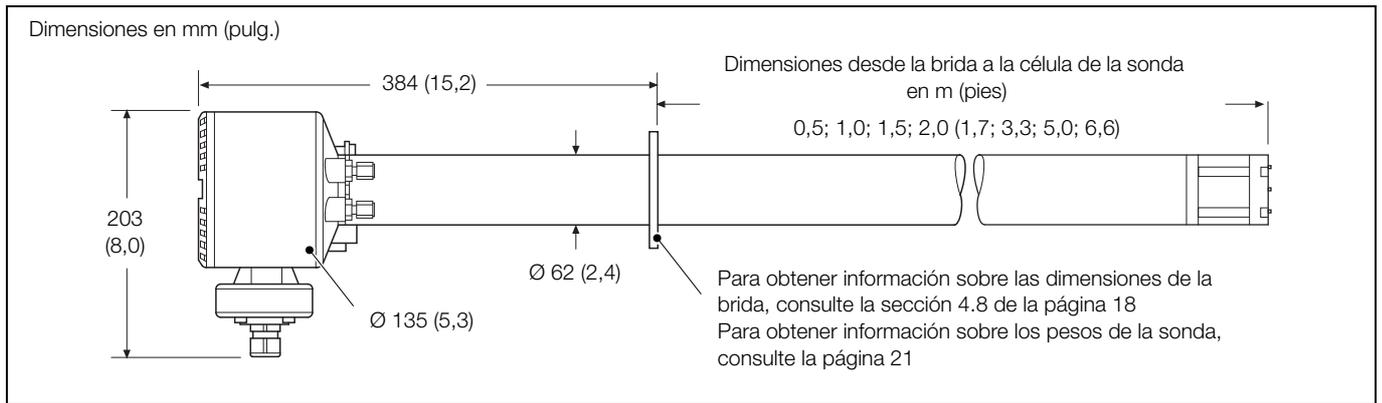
Dimensiones generales: sonda remota Endura AZ30
